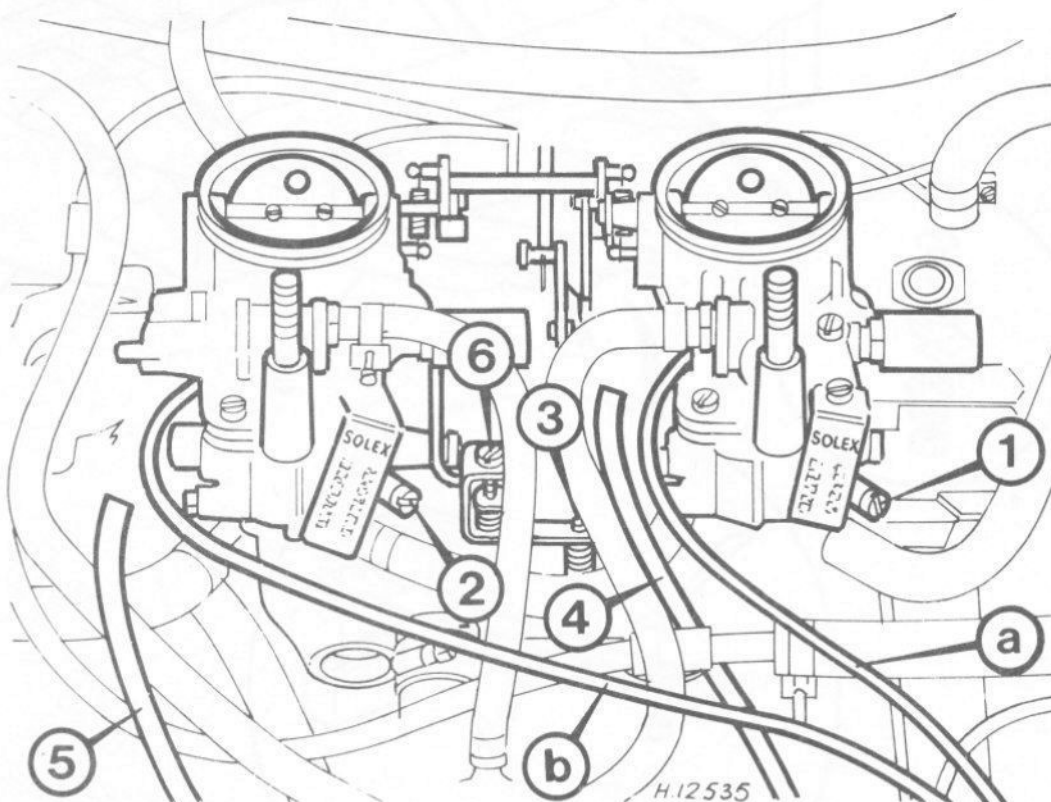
Positions des vis de réglage sur le carburateur Solex 35 PBISA 8 (Sec 10)
